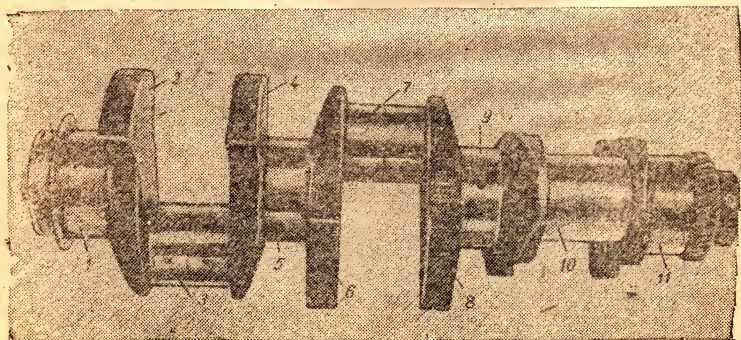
Коленчатый вал 6-цилиндрового V-образного дизельного двигателя:
